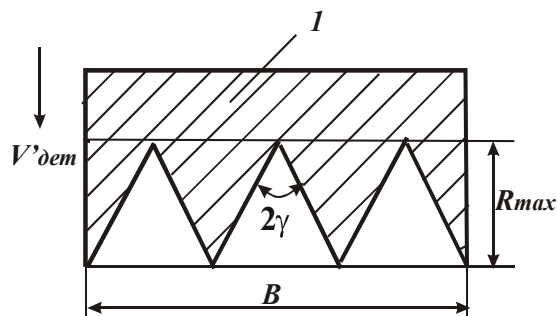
Схема образования шероховатости поверхности: 1 – обрабатываемый материал
